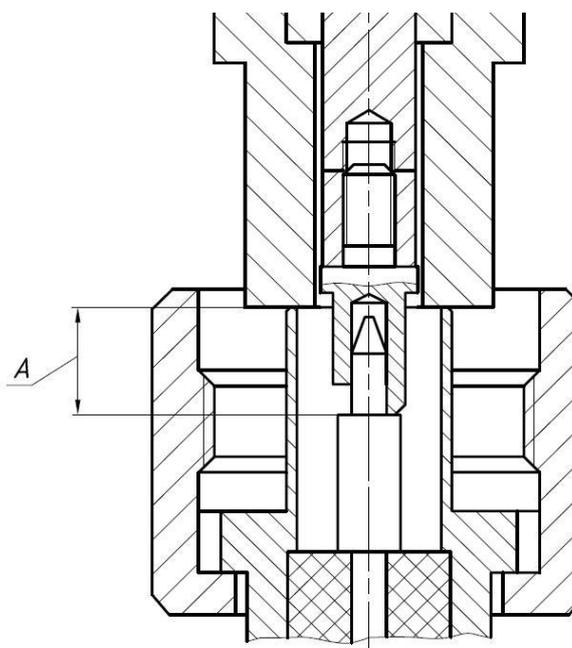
Проверка размера «А» соединителя «вилка»
